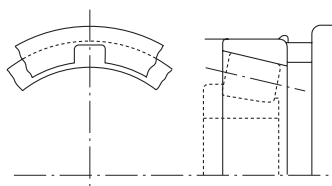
Канавки в корпусе конического роликоподшипника для демонтажа
